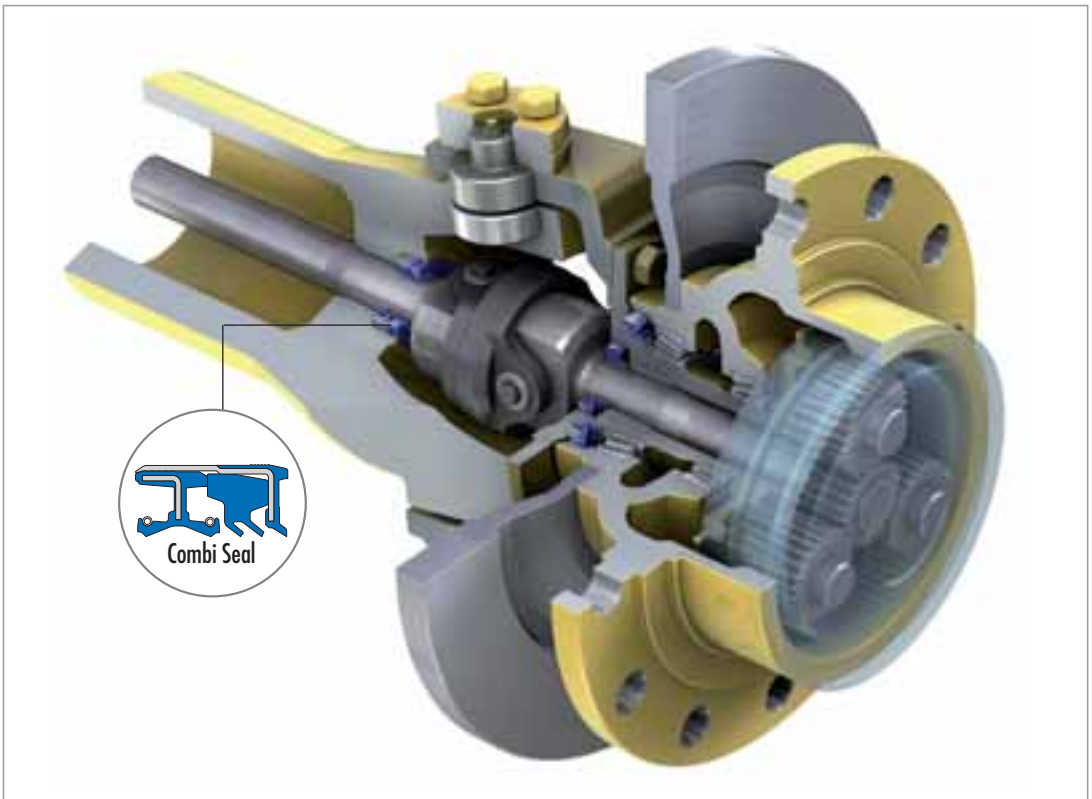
Simmerring Combi Seal in angetriebenen Achsen
